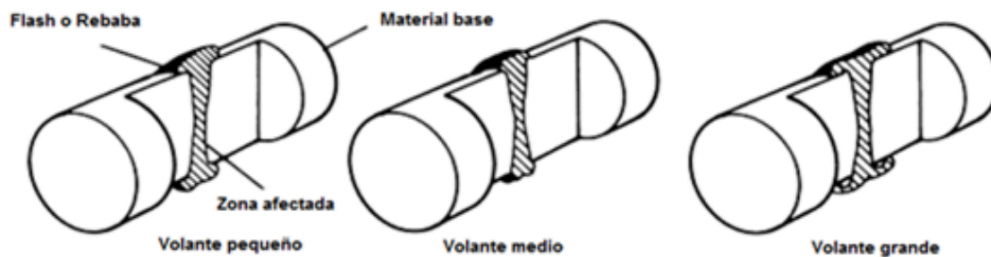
Sección de soldadura por inercia con diferentes tamaños de volante. [30]
